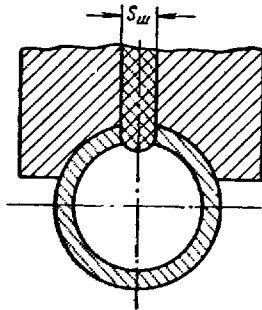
Форма направляющей шайбы в направляющих роликах сварного стана
